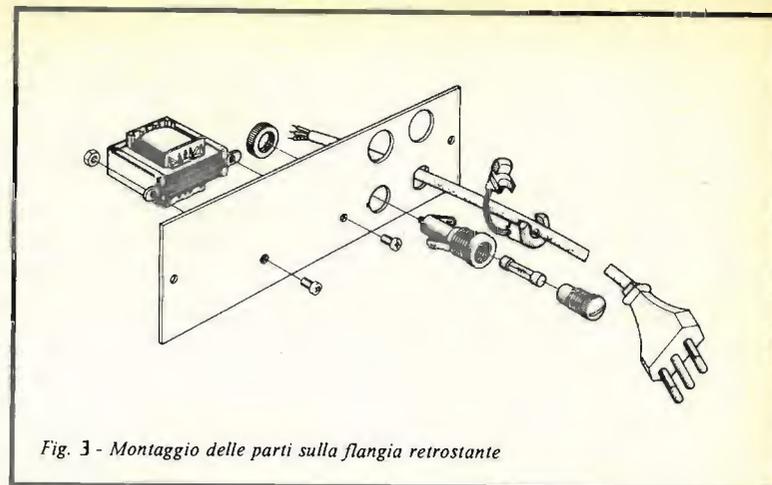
Montaggio delle parti sulla flangia retrostante
